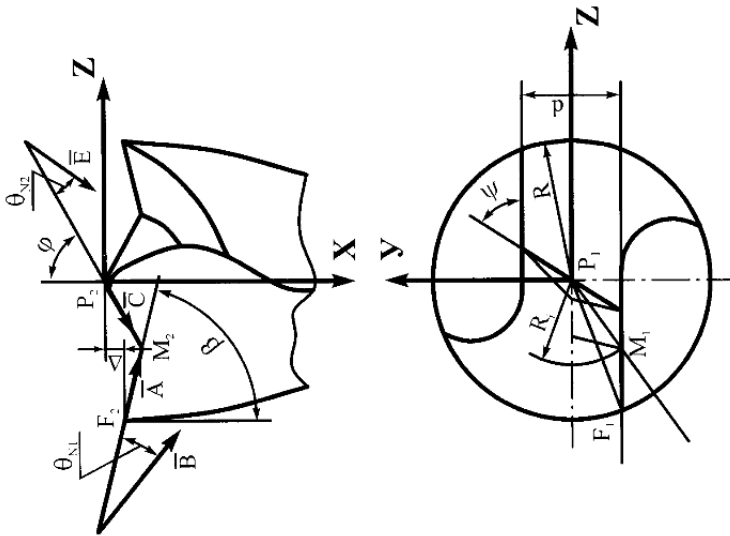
Геометрия сверла с подрезающими режущими кромками
